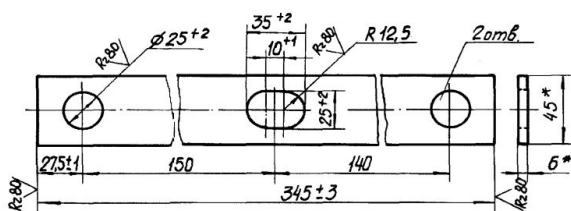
Планка стопорная для рельсов Р50 СИ-50-2
